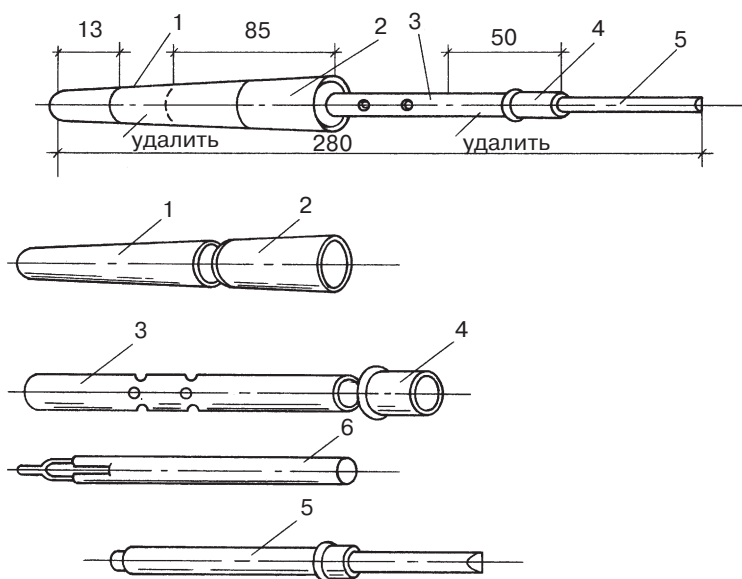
Электропаяльник ЭПСН-40: 1 — верхняя часть ручки; 2 — нижняя часть ручки; 3 — кожух; 4 — заглушка; 5 — жало с трубкой держателя; 6 — нагревательный элемент
